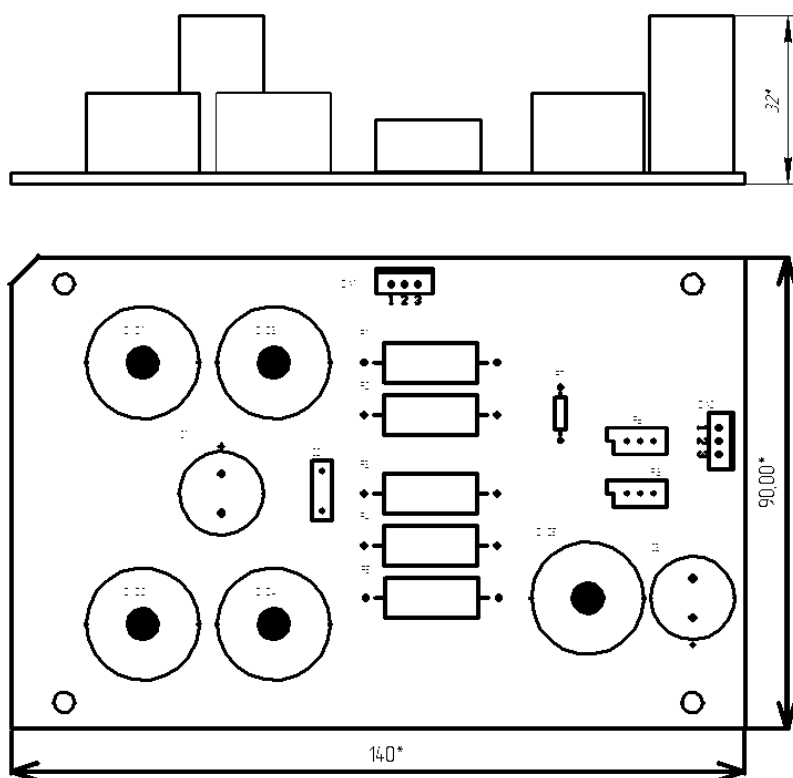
Эскиз сборочного чертежа печатной платы
